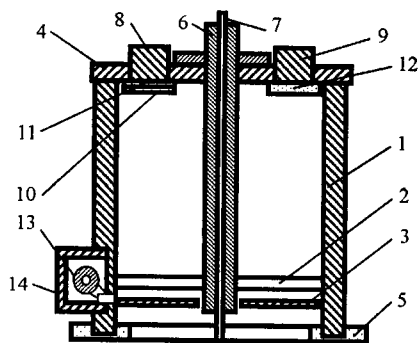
Фотометрическая головка с подстраиваемым углом зрения: 1 – металлический цилиндр; 2 – светорассеивающая пластина; 3 – регулируемая диафрагма; 4 – крышка цилиндра; 5 – кольцевое уплотнение (антисептическая прокладка); 6 – верхний конец направляющей трубки; 7 – осветительный световод; 8, 9 – фотоприемники (6 шт.); 10 – узкополосный светофильтр (5 шт.); 11 – нейтральный светофильтр; 12 – обрезывающий светофильтр; 13 – шаговый двигатель диафрагмы; 14 – защитный кожух двигателя
